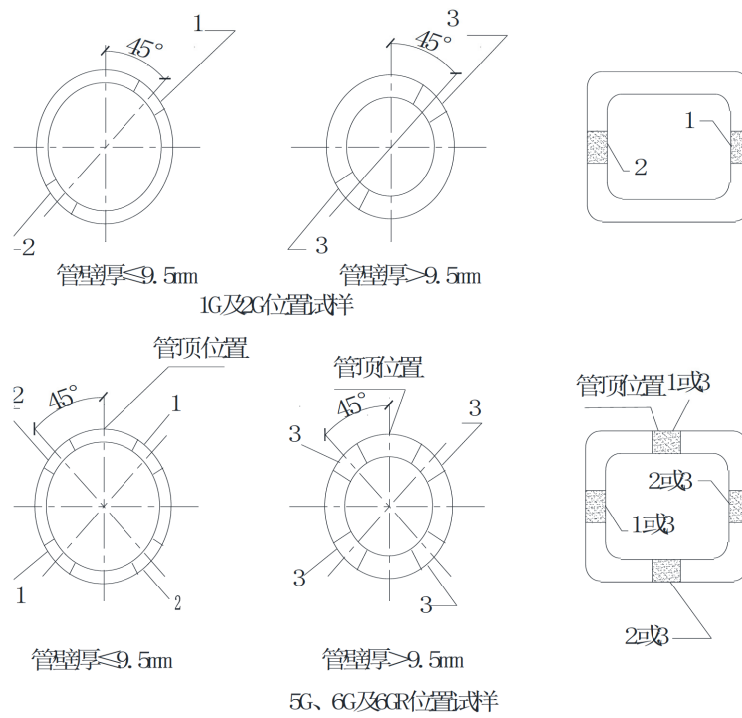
各种焊接位置管材试件取样位置
